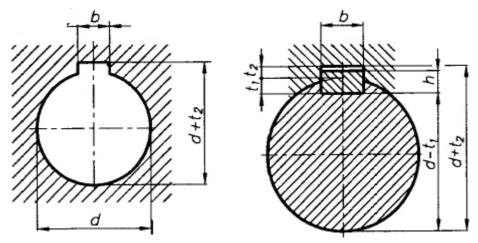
Схема расположения шпоночного паза на зубчатом колесе
